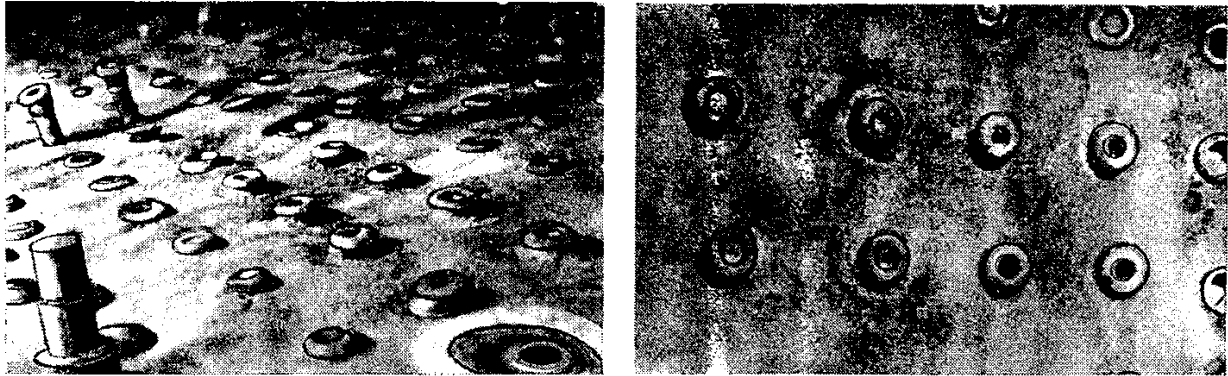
Abzehrung einer kupfernen Feuerbüchse durch Schwefeldioxid
